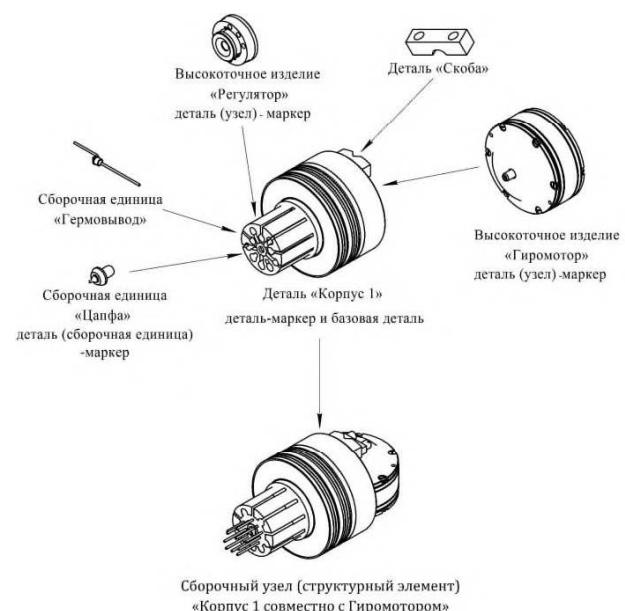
Пример разбиения сборочного узла «Корпус 1» совместно с Гиромотором», начинающегося с базовой детали
